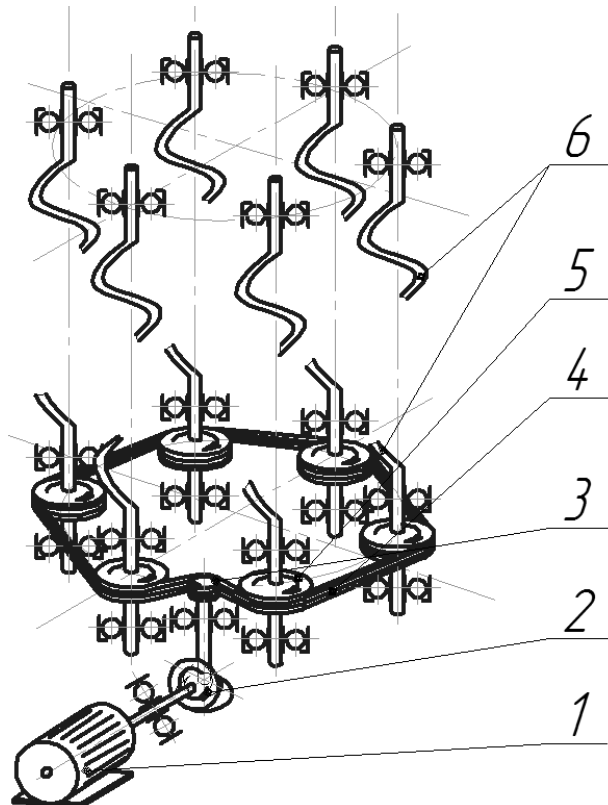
Кінематична схема приводу сушарки для визначення ККД:
